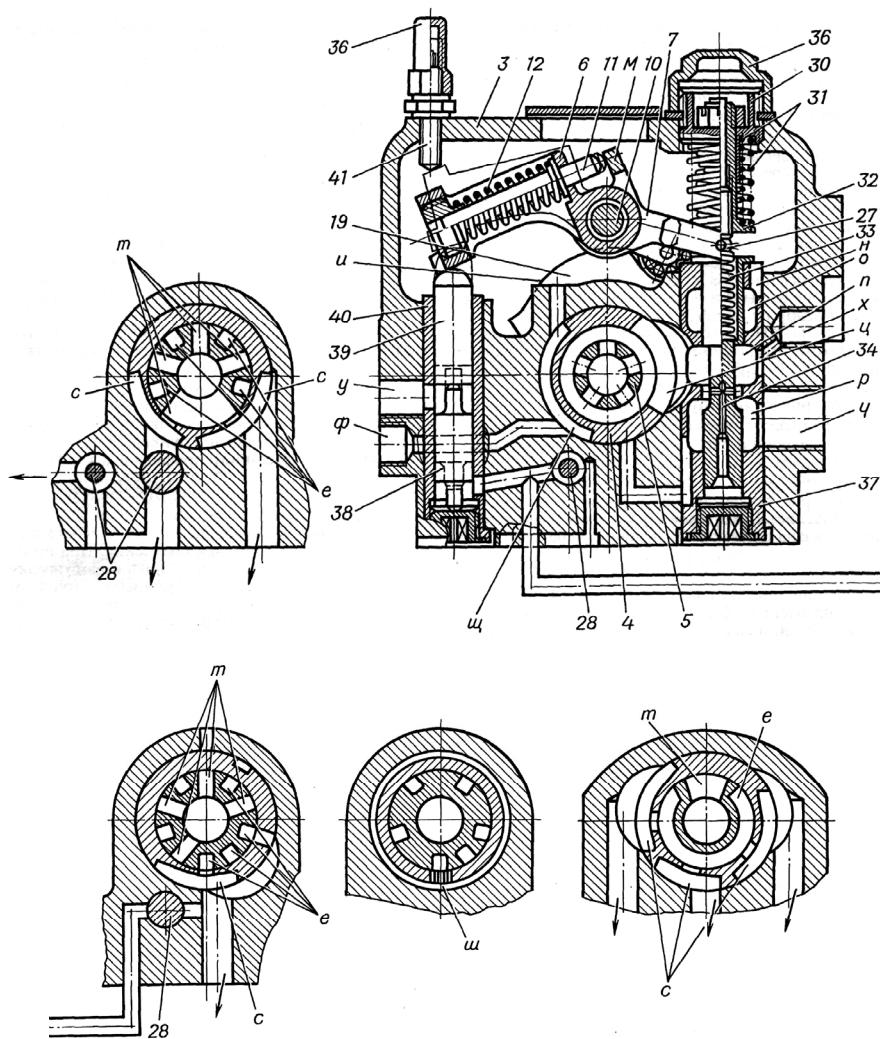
Механизм распределения: 3 – картер; 4 – втулка поворота; 5 – пробка; 6 – рычаг повышения давления; 7 – вильчатый рычаг; 10 – вал; 11 – шток; 12, 33 – пружины; 13 – зубчатый сектор; 19 – кулак поворота; 27 – сухарь; 28 – блокировочный золотник; 30 – регулировочная втулка; 31 – возвратные пружины; 32 – тарелки; 34 – золотник регулятора давления; 36 – колпачок; 37, 40 – втулки; 38, 39 – золотники повышения давления; 41 – регулировочный винт; *e* – паз сливной пробки; *u* – наружный профиль кулака поворота; *m* – упор вильчатого рычага; *n* – сливное отверстие (показано условно); *o* – верхняя полость втулки; *p* – средняя полость втулки; *p* – нижняя полость втулки; *c* – пазы для подвода масла к бустерам во втулке поворота; *m* – пазы в пробке подвода масла к бустерам; *y*, ϕ – отверстия для подсоединения трубопровода повышения давления; *x* – отверстие для подсоединения датчика манометра; *ц* – канал подвода масла к пробке; *ч* – отверстие для подвода масла из гидросистемы; *ш* – кольцевая проточка втулки поворота; *щ* – паз управления повышения давления на забегающем борту
